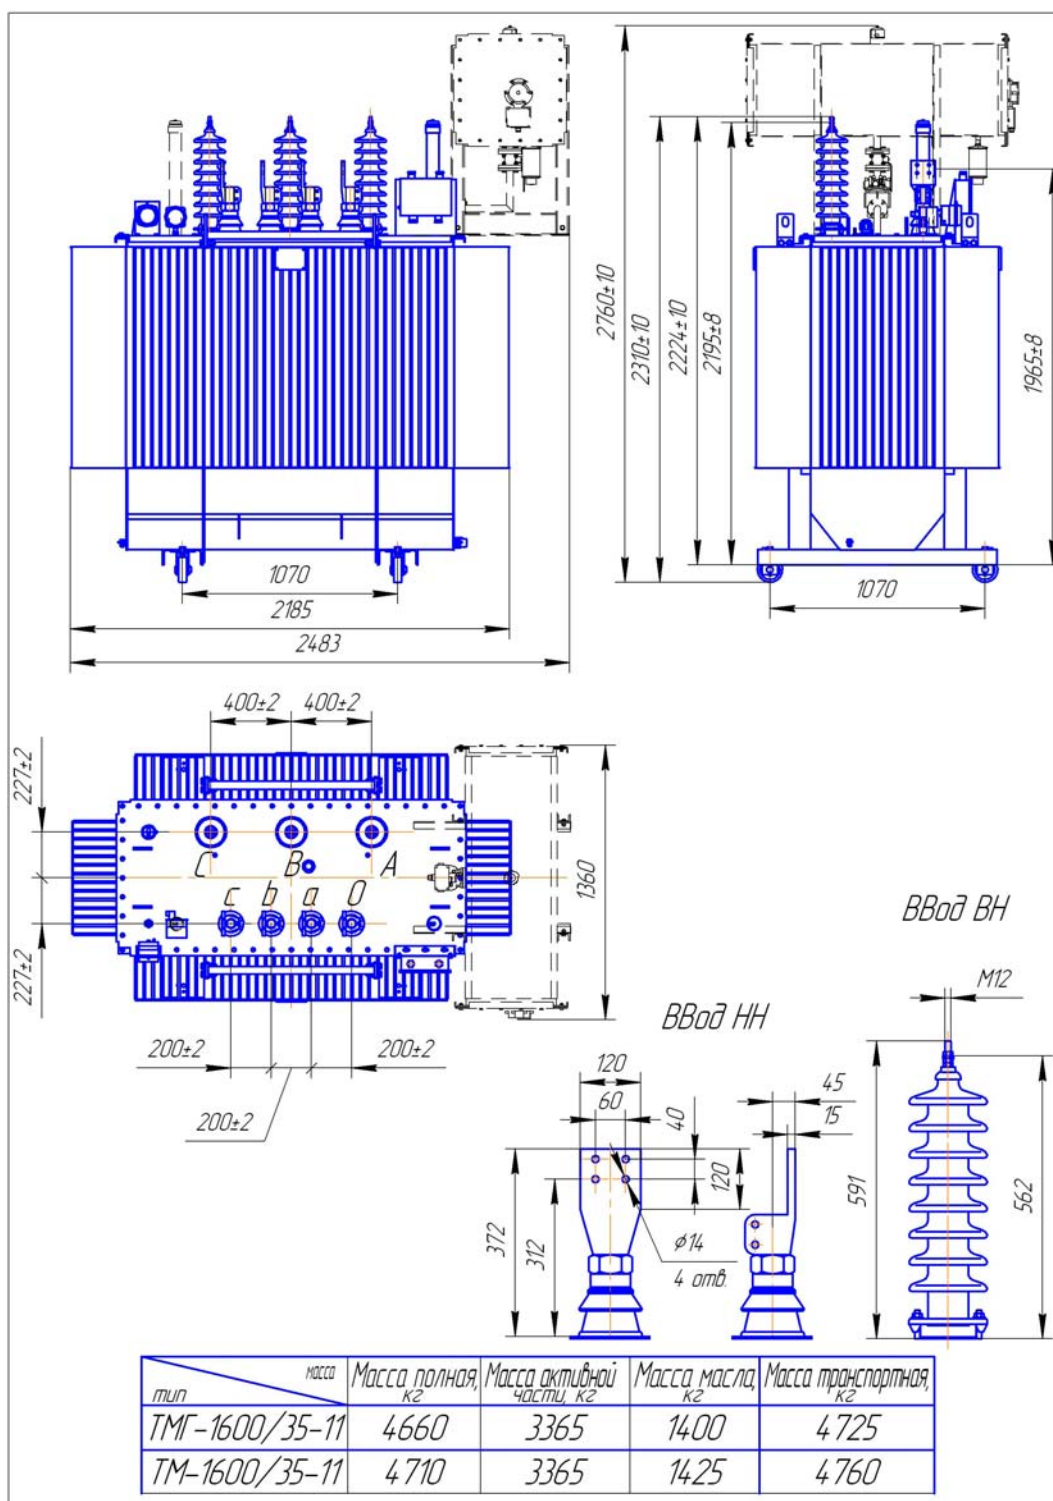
Габаритные, установочные и присоединительные размеры трансформатора ТМ(Г) - 1600/35-11
